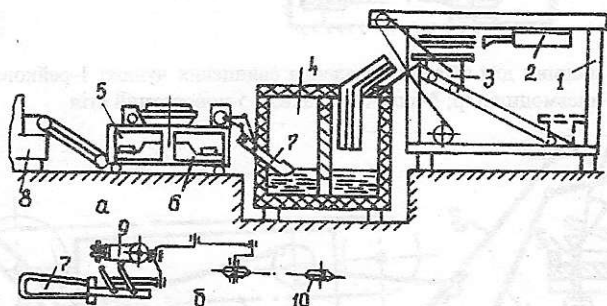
Схема автоматизованої лінії плавки і розливки катодного цинку (а) і механізму управління ложкою (б): 1-завантажувальний пристрій; 2-зптовхувач листів; 3-підйомний стіл; 4-плавильна піч; 5-розливна машина; 6-кронштейн з виливницями; 7-заливна ложка; 8-укладальник чушок; 9-копір; 10-приводна зірочка
